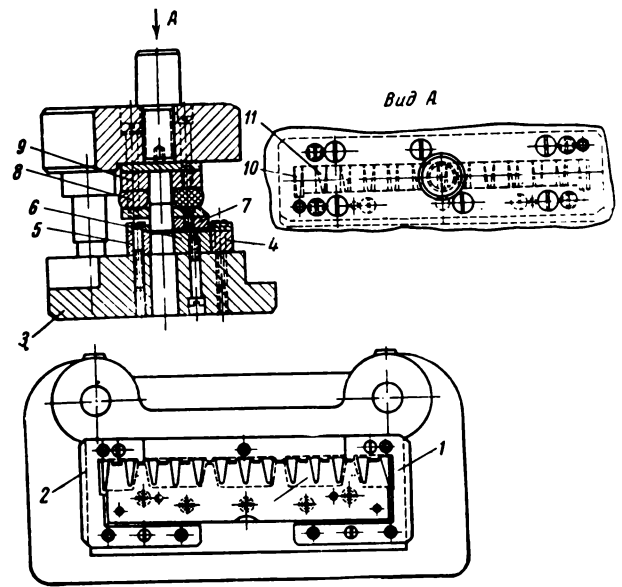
Штамп для вырубке заготовки манжеты.
